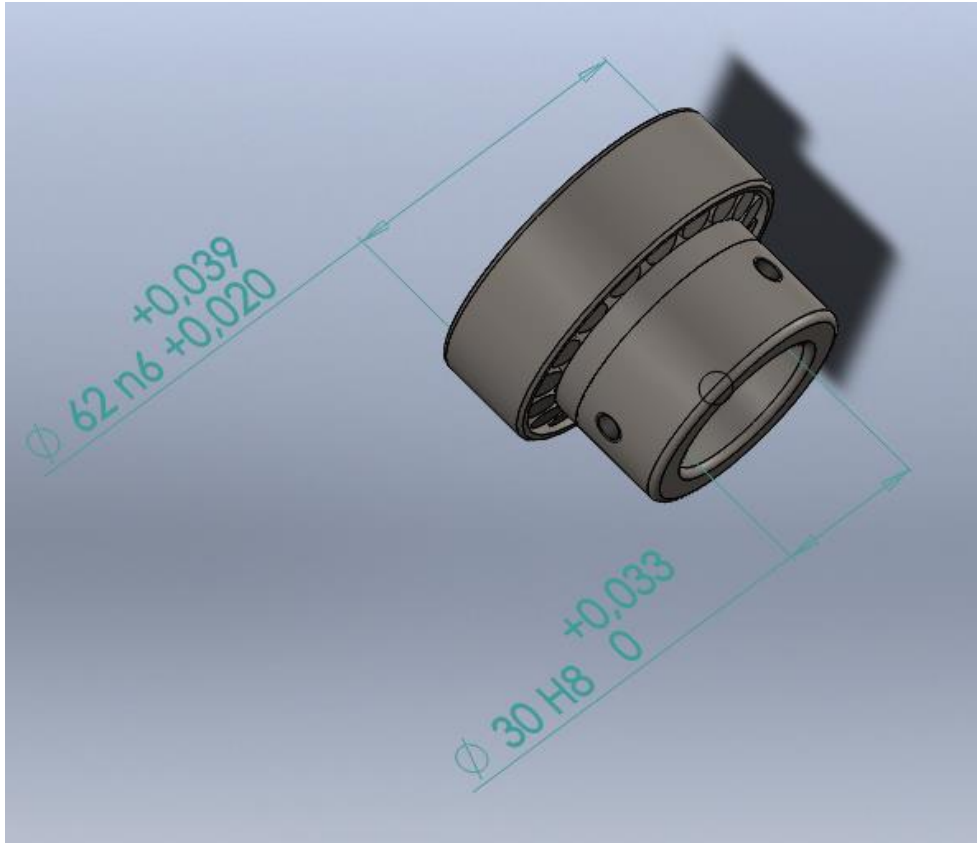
detalle tolerancias rodamiento. Fuente: propia.
